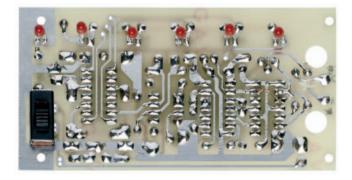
Photo d'un des prototypes de la platine du Diode Speed Tester, vu côté soudures.
